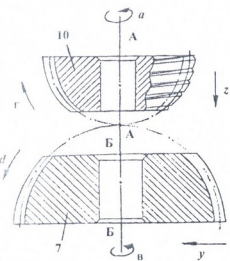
Схема нарезания сферического зубчатого колеса
